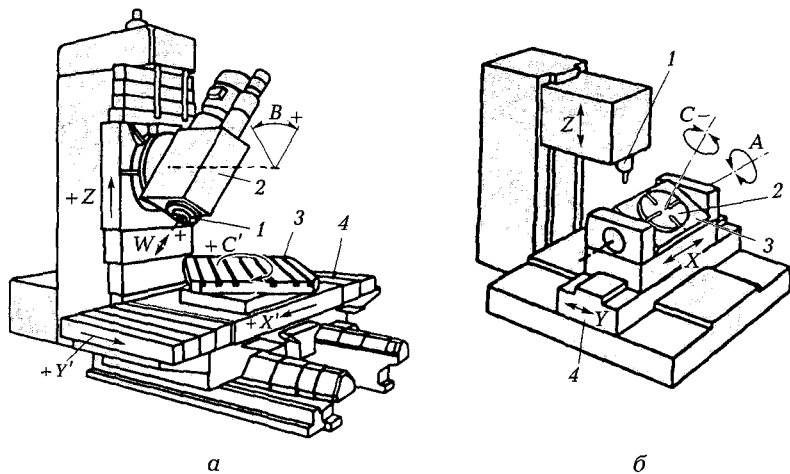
Многоцелевые станки для обработки сложных объемных заготовок:
